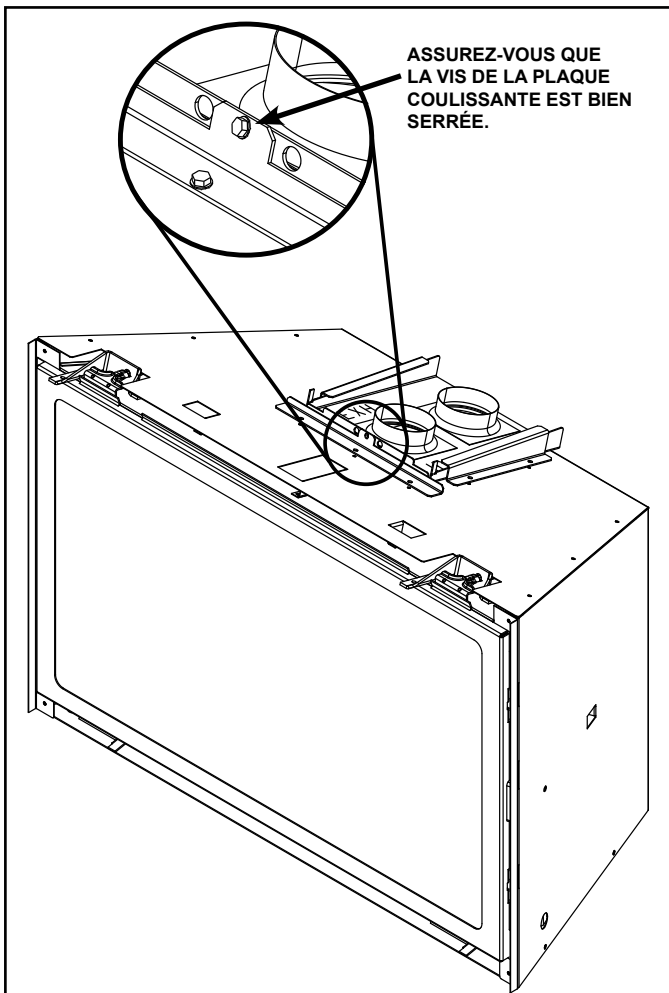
Détails sur la vis de la plaque coulissante du col
